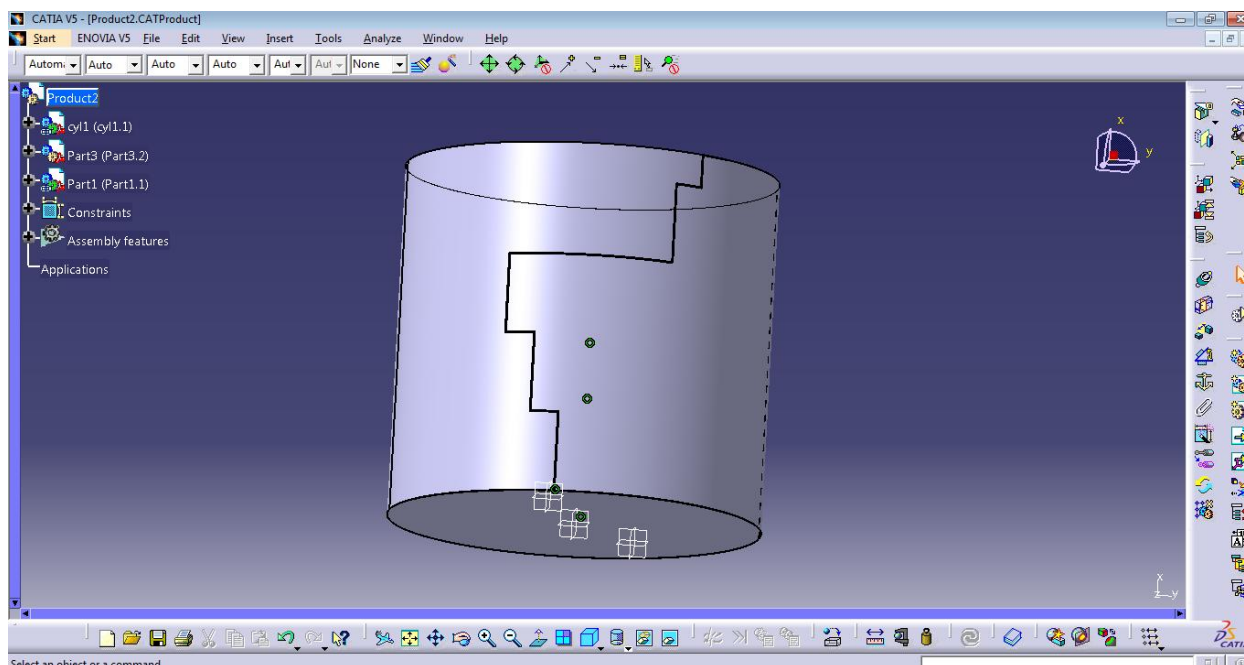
Загальний вигляд просторової моделі резервуару зі зварним швом.
